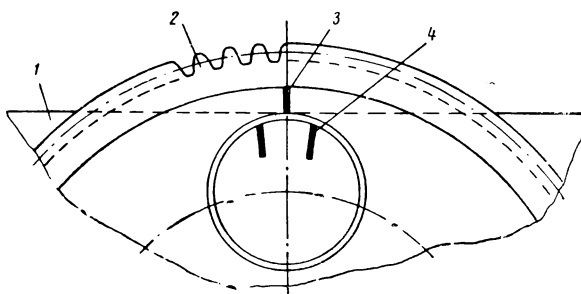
Положение шестерни верхней блокировки относительно рамы при фиксации вала главного контроллера ЭКГ-8 на позиции:
